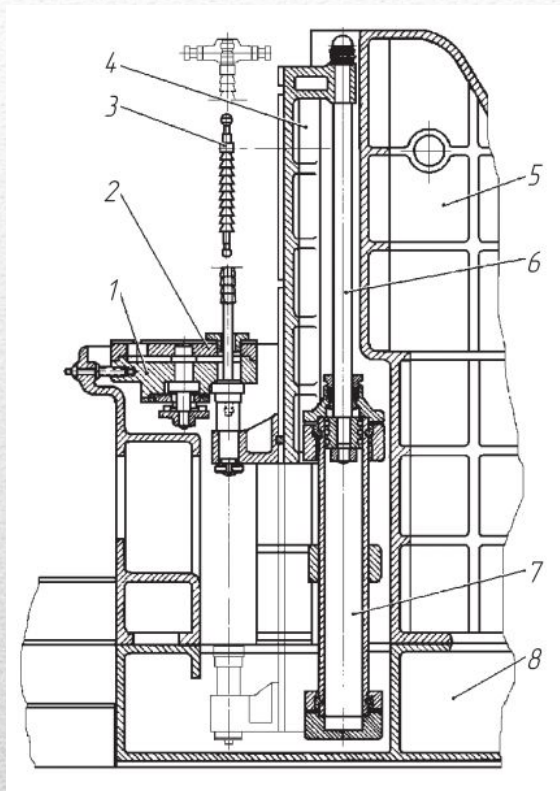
Схема станка модели 7751У для внутреннего протягивания:
